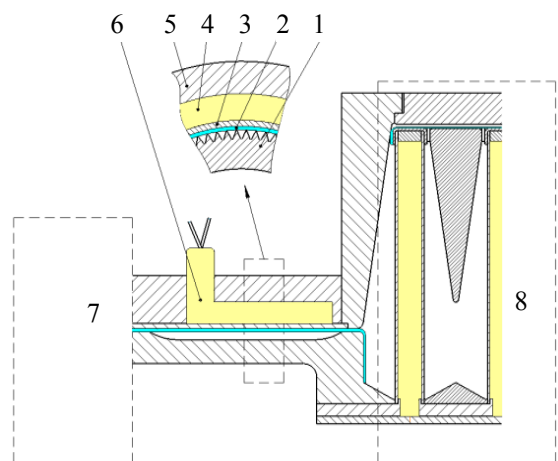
Схема стандартного узла отключения ДВМГ от СВМГ: 1 – медный цилиндр; 2 – лавсановый изолятор; 3 – медный цилиндр-лайнер; 4 – цилиндрический заряд ВВ; 5 – стальной корпус; 6 – система инициирования заряда из 24-х электродетонаторов; 7 – СВМГ; 8 – ДВМГ.
